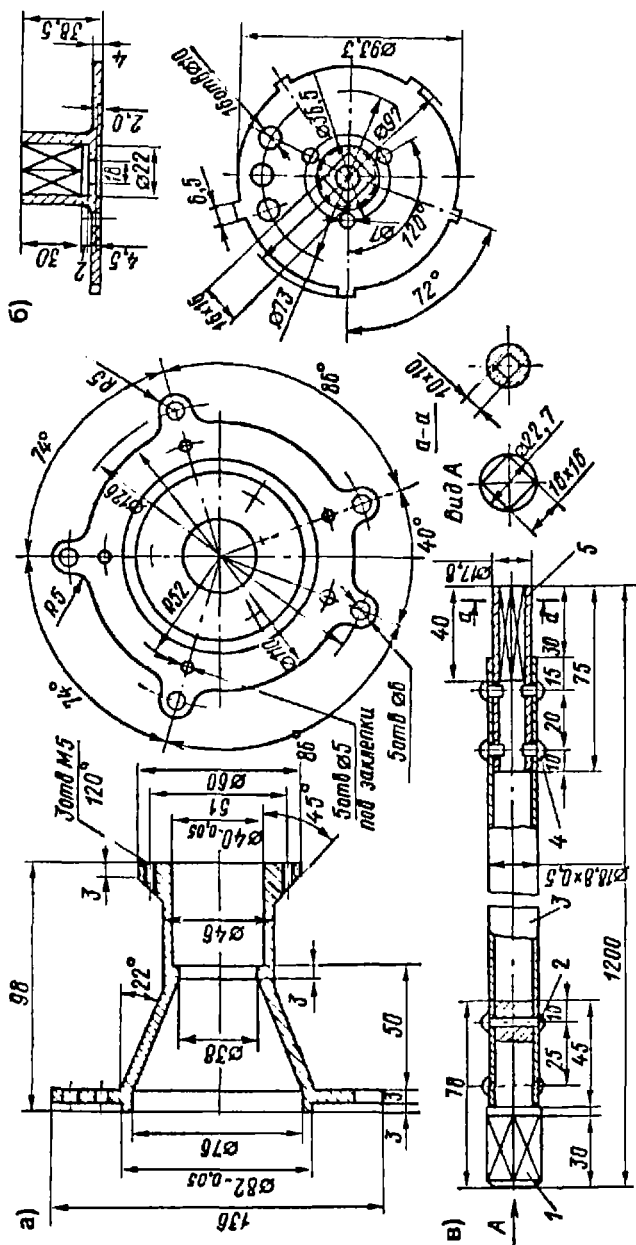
Конструкция основных деталей силового передаточного механизма: а — конусный переходник, дюраля; б — шлицевой диск, сталь 50; в — ведущий вал. 1 — наконечник, сталь У8-У12; 2 — заклепка, сталь; 3 — труба, дюраль; 4 — винт М4; 5 — наконечник, сталь.
